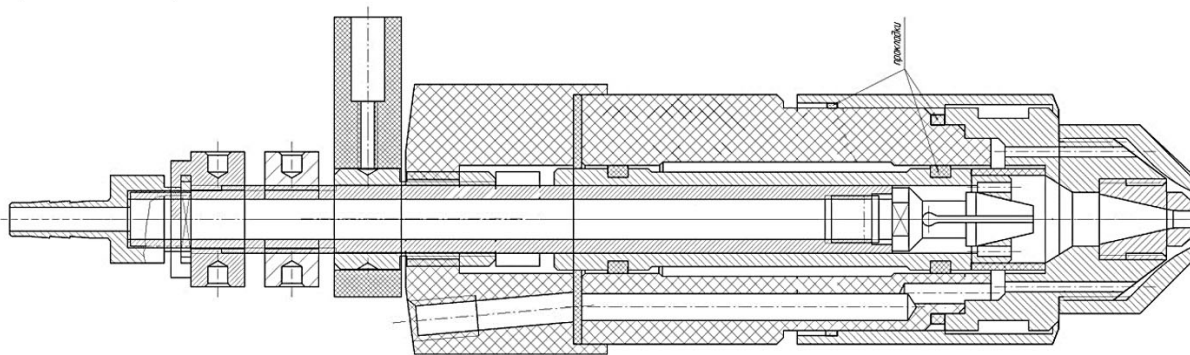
Сварочный плазмоторн (сборочный чертеж)
